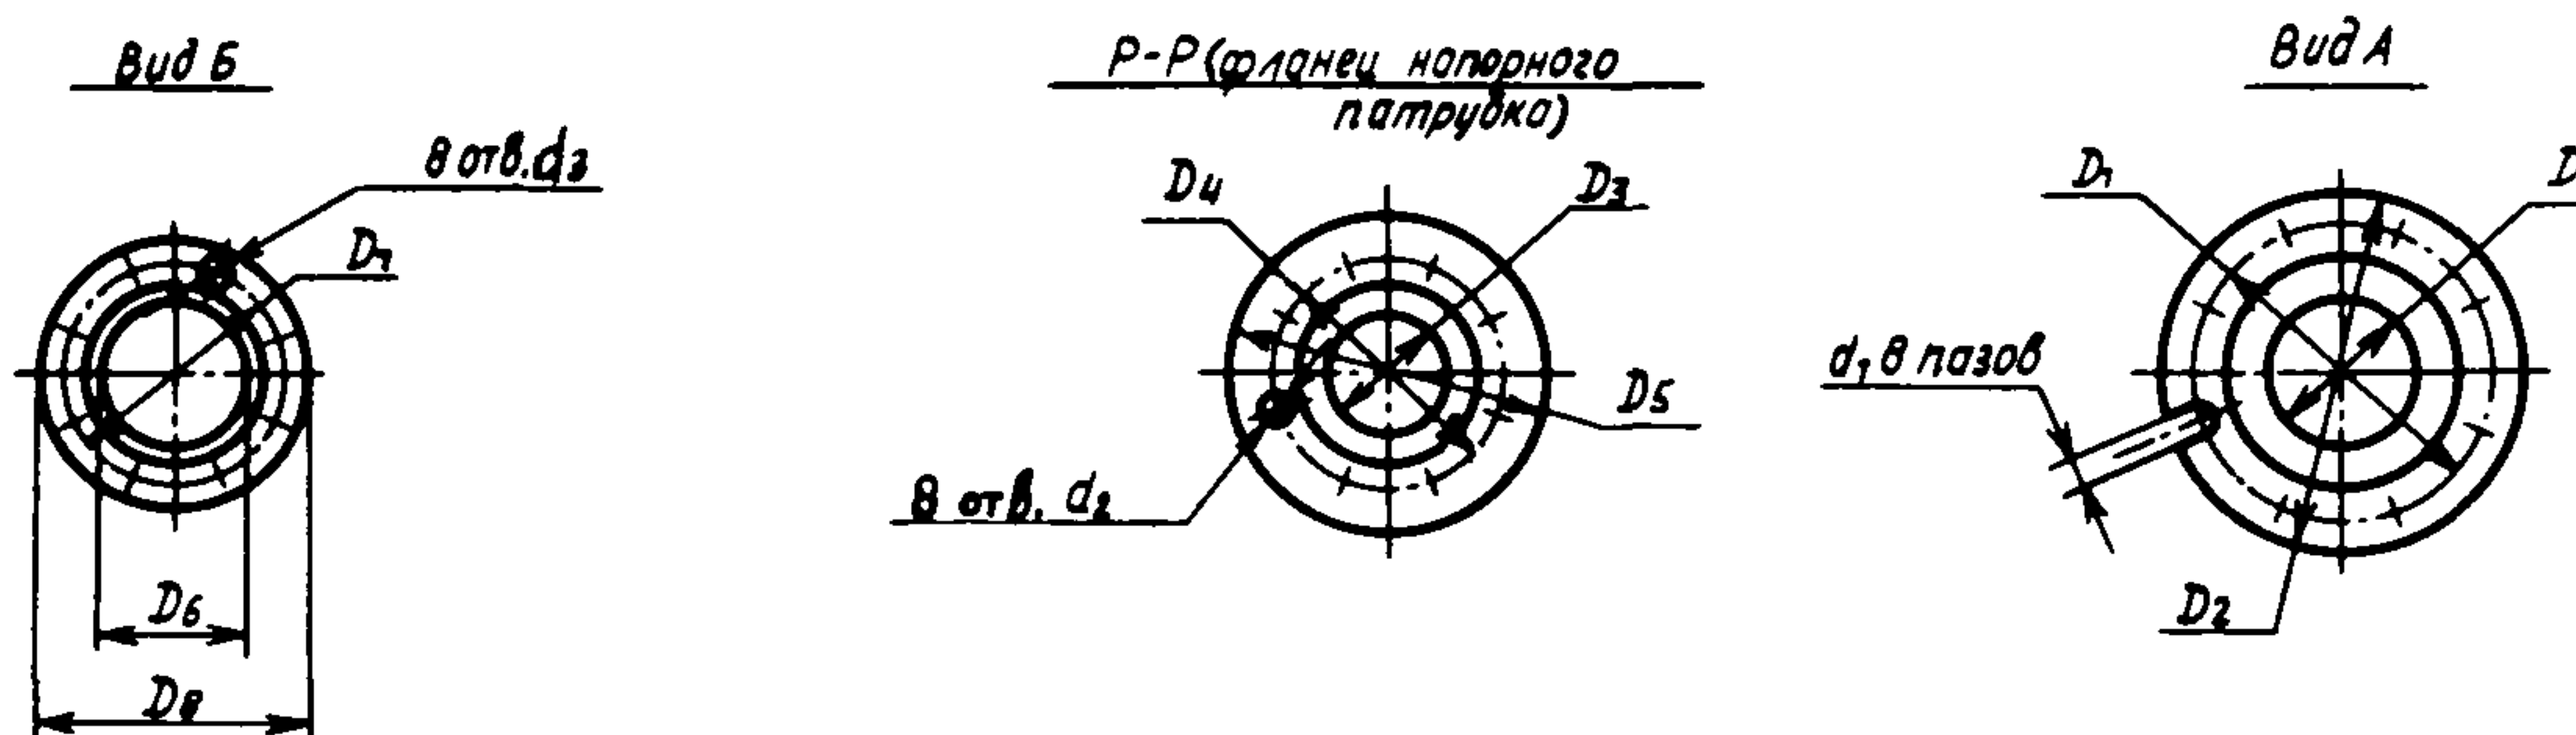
Присоединительные размеры патрубков насосов типа НПБР
